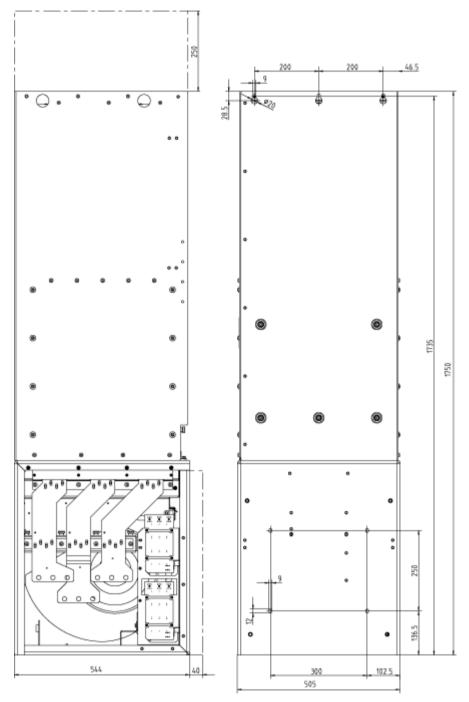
Габаритный чертеж активного интерфейсного модуля, типоразмер JI. Вид сбоку, вид сзади
